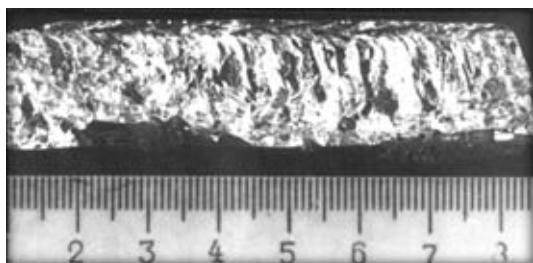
Внешний вид излома плоской заготовки хрома, выплавленной по схеме, представленной на рис. 1, *а
